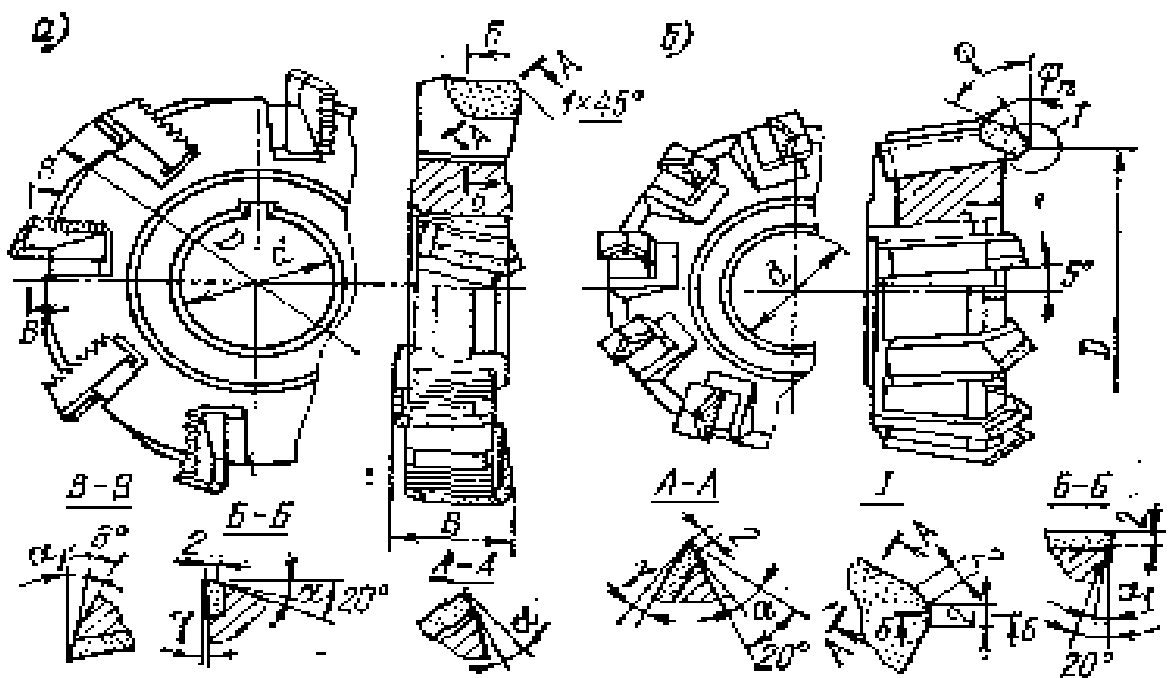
Збірні фрези зі вставними ножами, оснащеними пластинами з твердого сплаву
